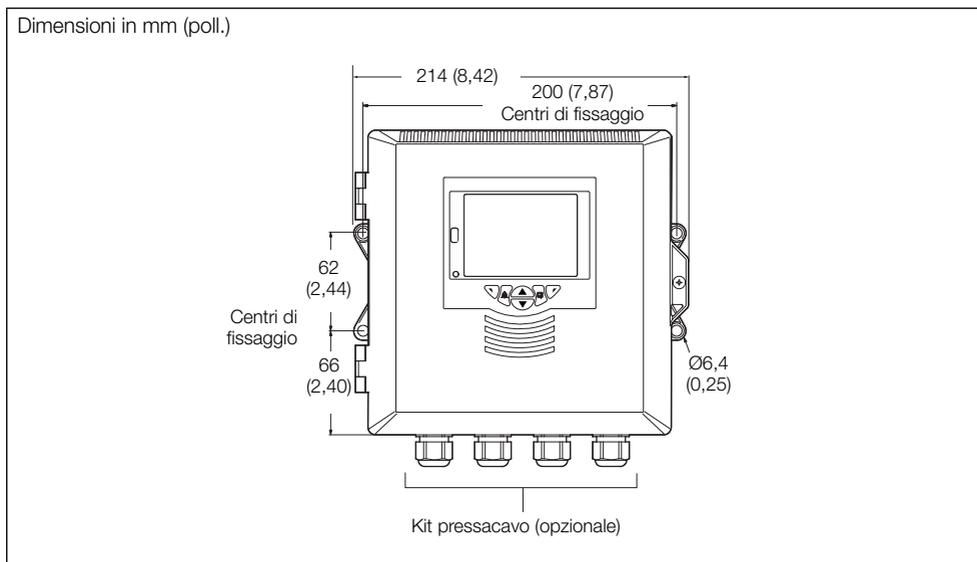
ControlMaster CMF310 per montaggio a parete
